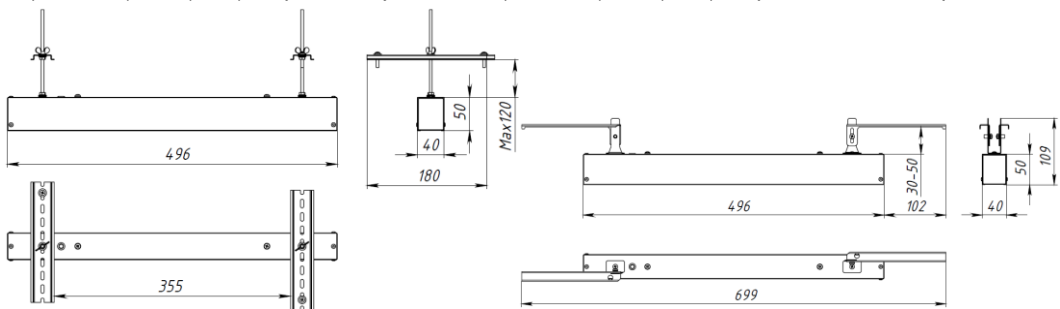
Габаритные размеры с креплением для реечного потолка.
